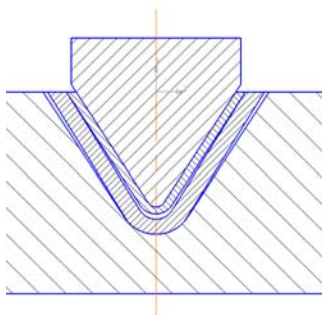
Схема штамповки, когда деталь частично касается упругого элемента
